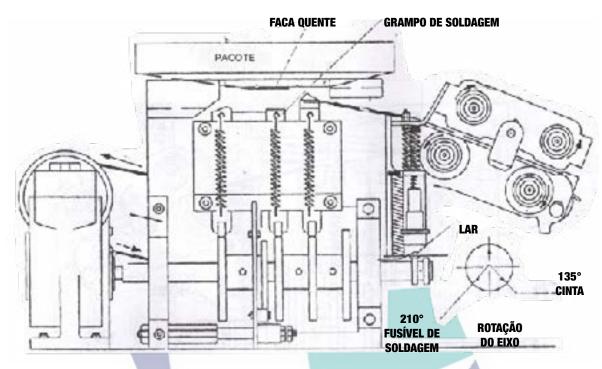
A CORREIA É CORTADA E A SOLDAGEM É FEITA
